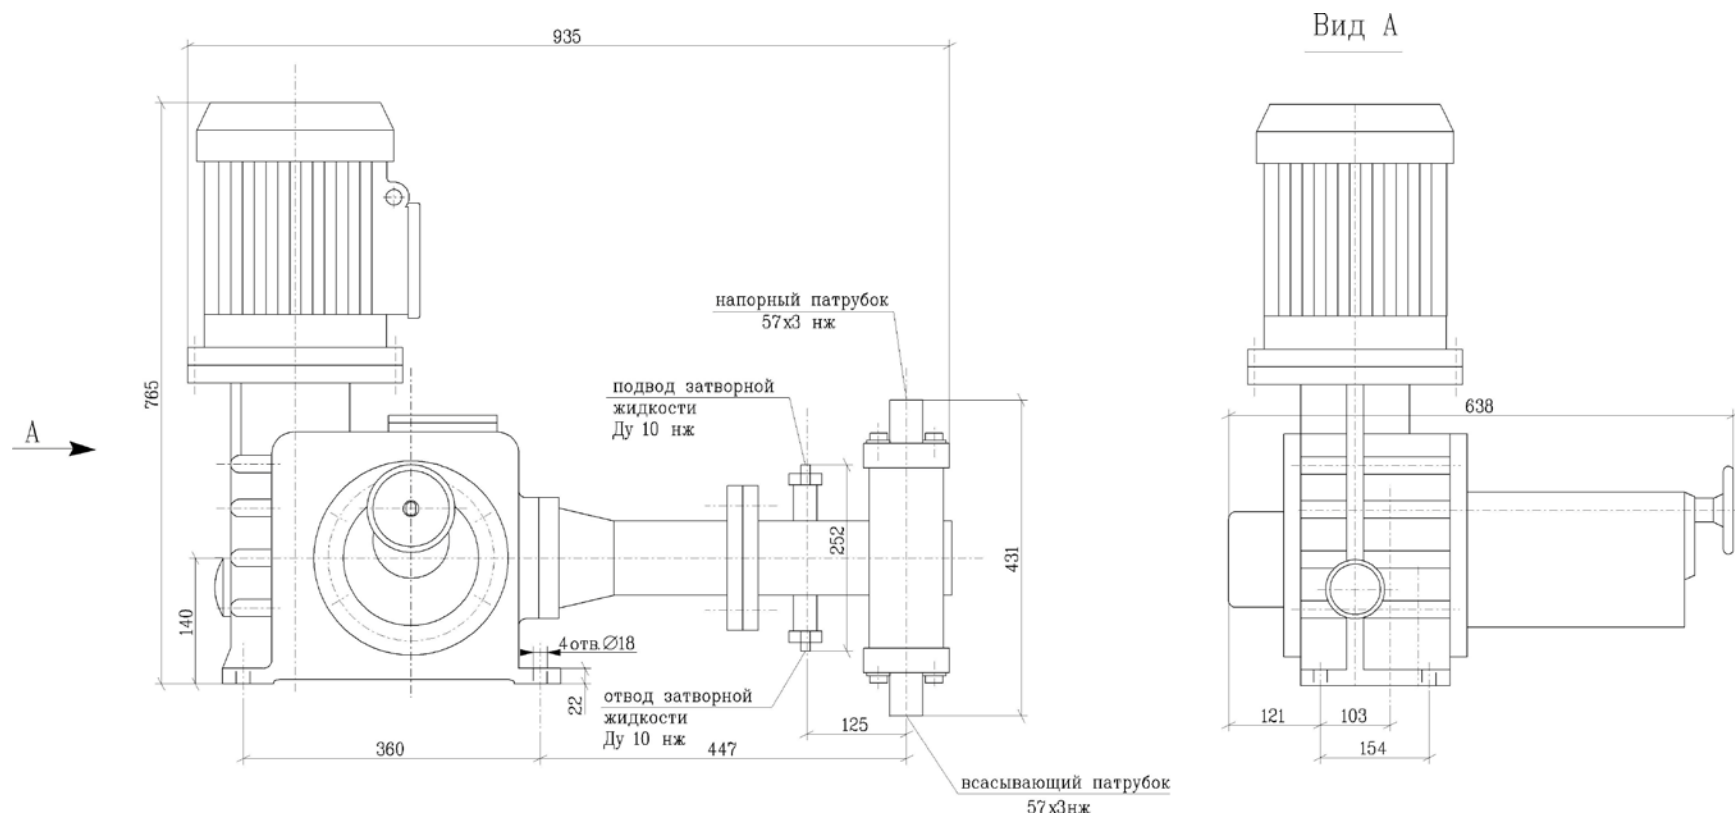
Габаритный чертеж насоса-дозатора щелочи LDP20AP001, LDP20AP002
